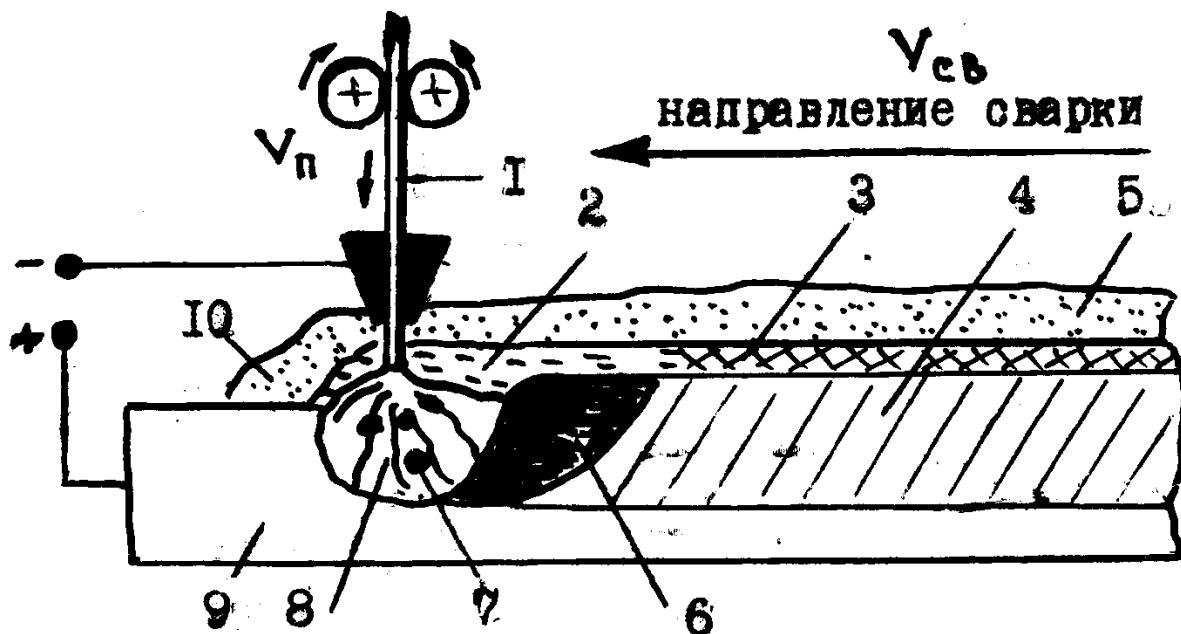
Схема автоматической сварки под флюсом. При горении дуги развивается высокая температура - около 6000 °С. Под действием этой температуры расплавляются электрод, основной металл изделия в зоне горения дуги и часть флюса, окружающего дугу. Расплавленный флюс образует вокруг дуги жидкую оболочку 2.
